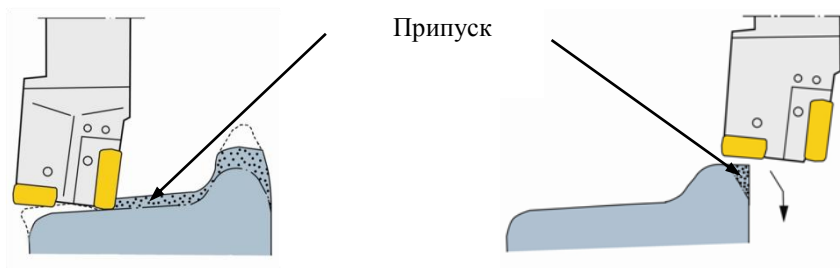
Багаторізева схема обробки профілю колісної пари
